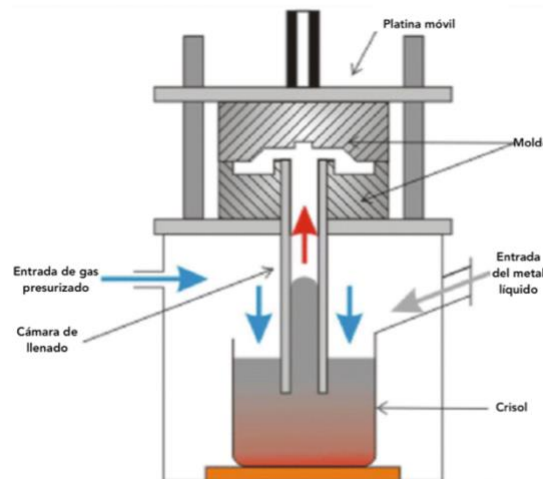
Fundición por llenado a baja presión. Adaptado de [3].
